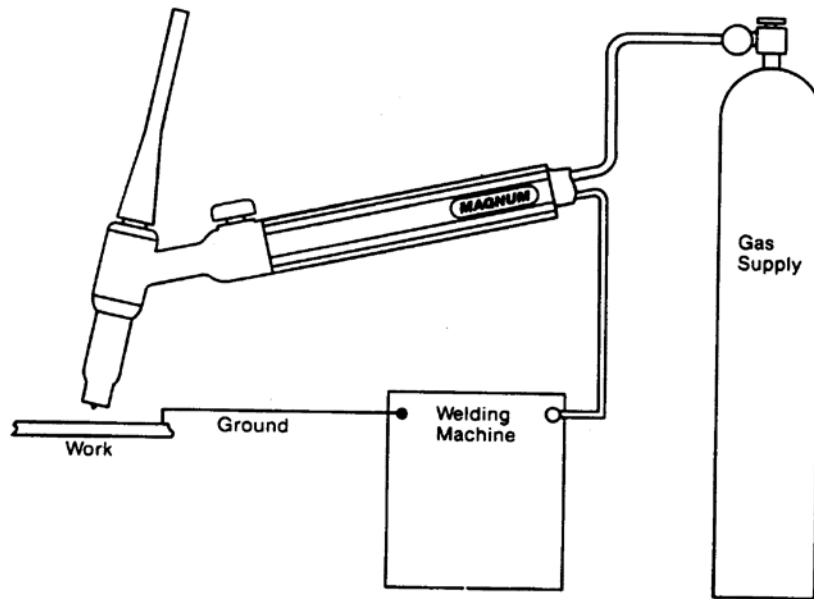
esquema básico de soldadura GTAW
